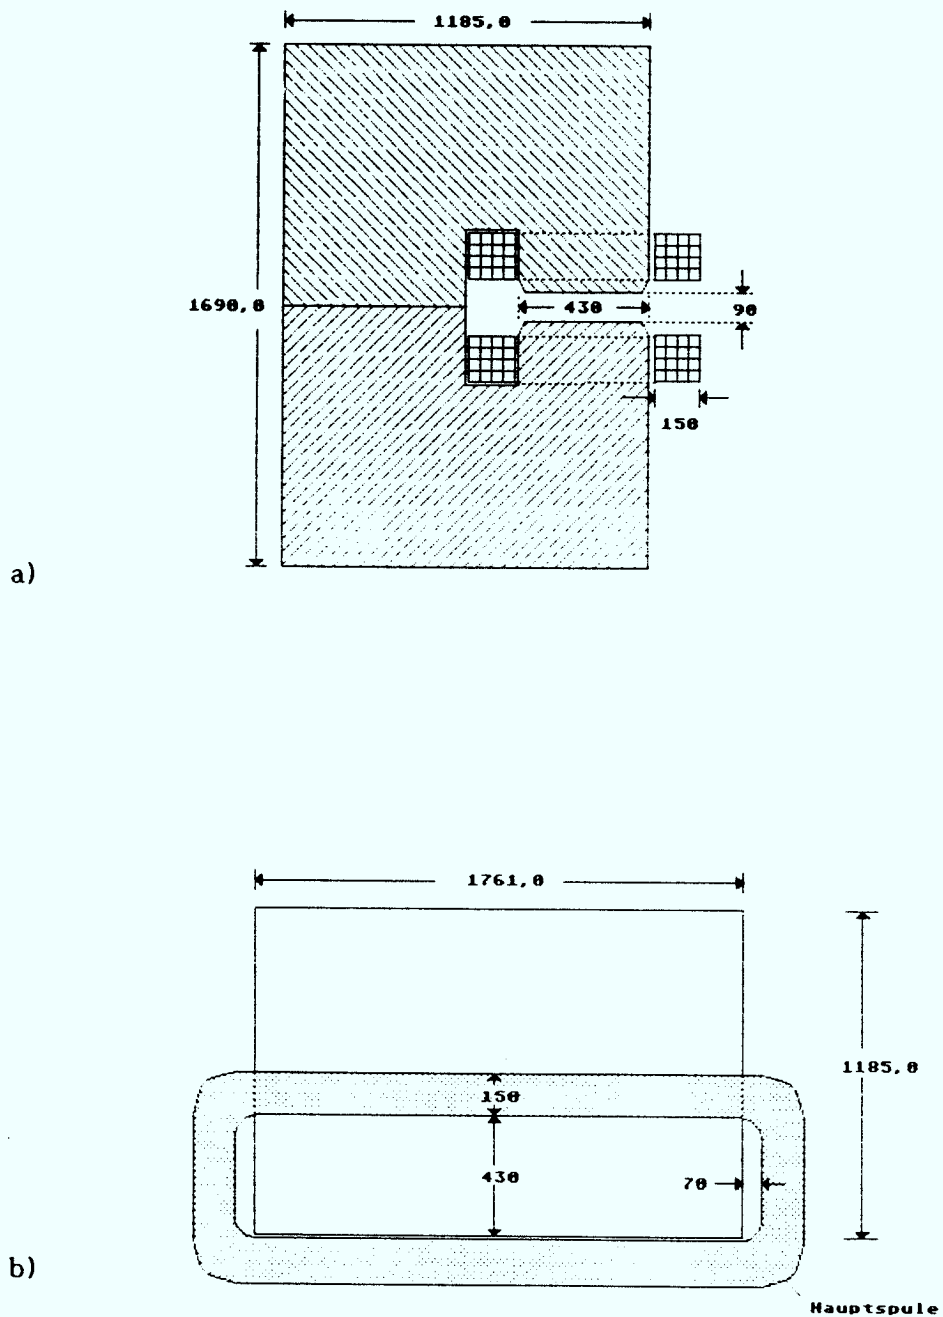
Geometrie eines COSY-Dipols. a) Seitenansicht, b) Draufsicht
